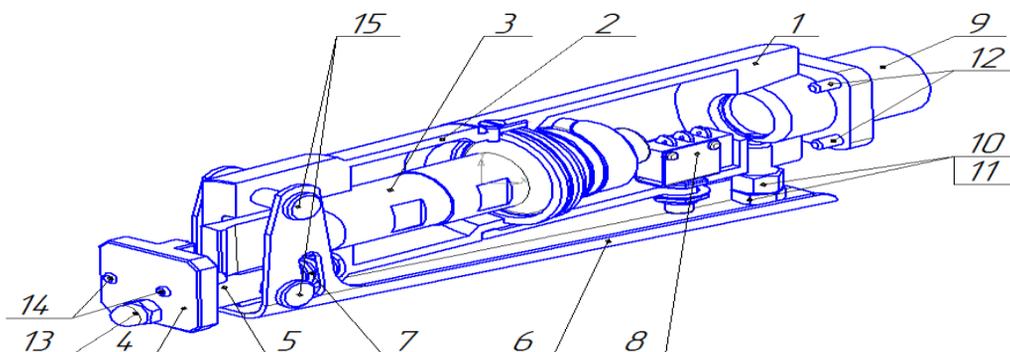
Ультразвуковое устройство для герметизации полимерных трубок
